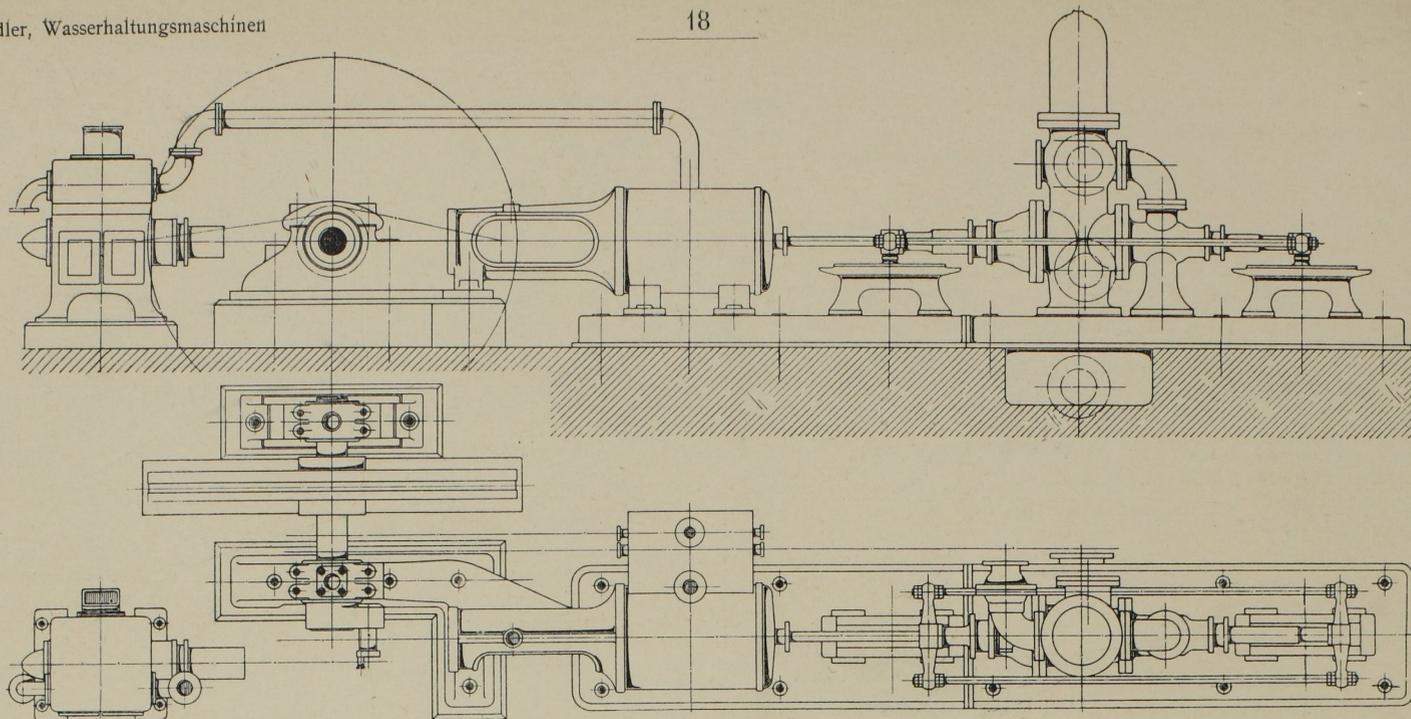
Seitenansicht und Grundriss der Maschine. Masst. 1:60.
